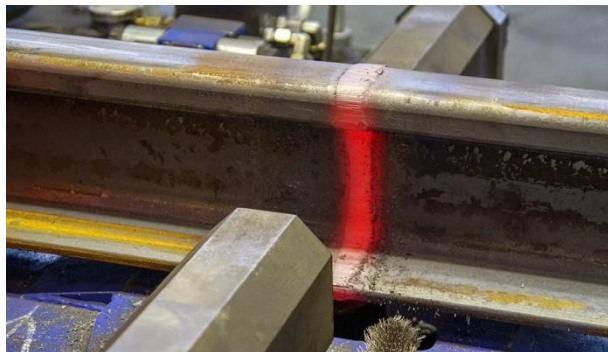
Удаление грата и выдавленного металла в сварном стыке
